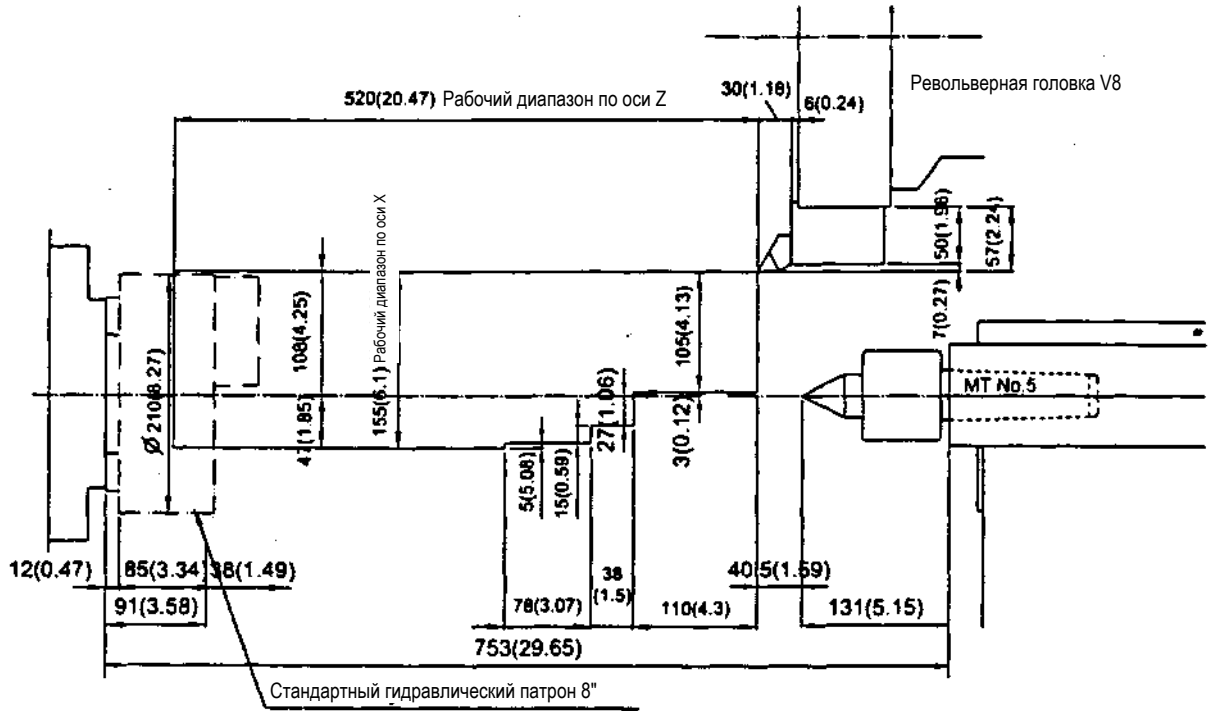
Схема рабочего диапазона (Резцедержатель внешнего диаметра (тип II))
